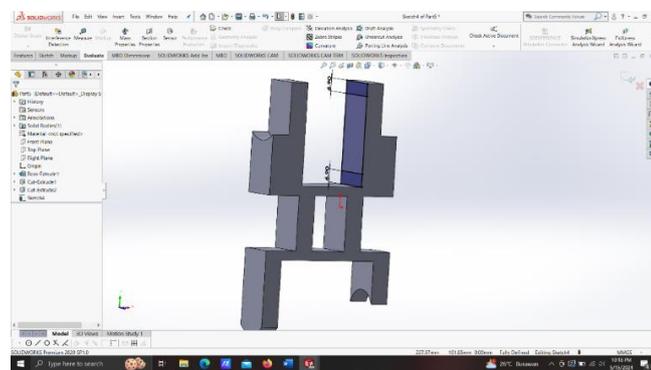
Extruded Cut* Pada Sisi Samping Kiri
